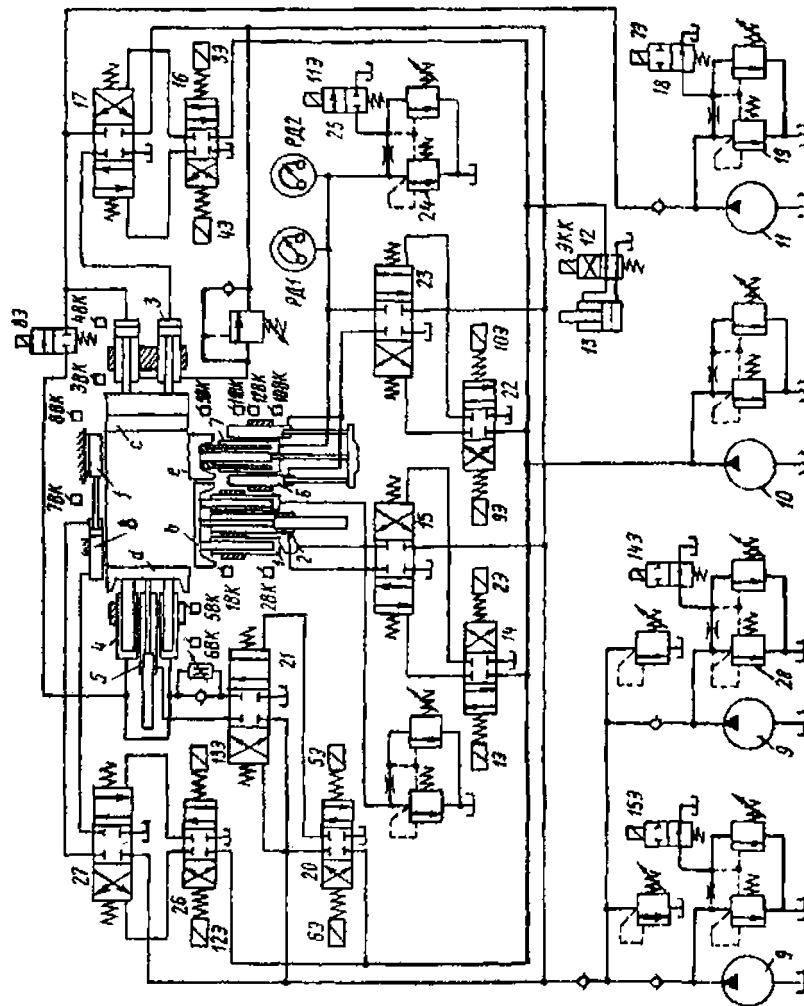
Гидравлическая схема пакегаировочного пресса ПГ-1500
